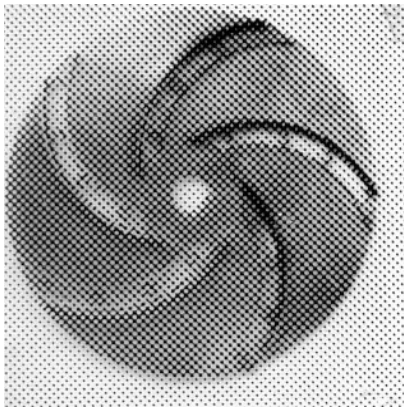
Загальний вигляд диска нового робочого колеса
